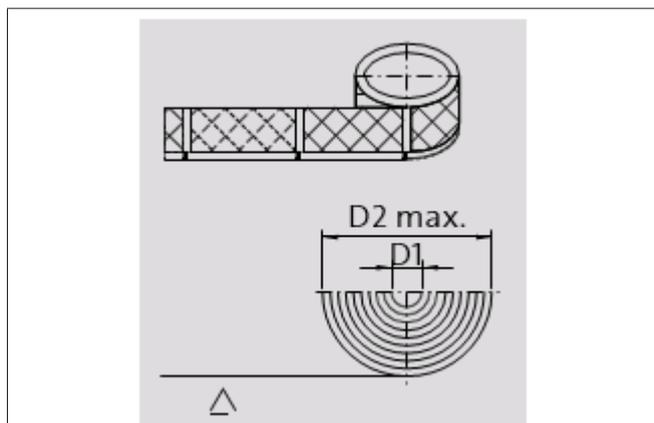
Sens d'enroulement des bobines pour sens de marche de la machine de gauche à droite
